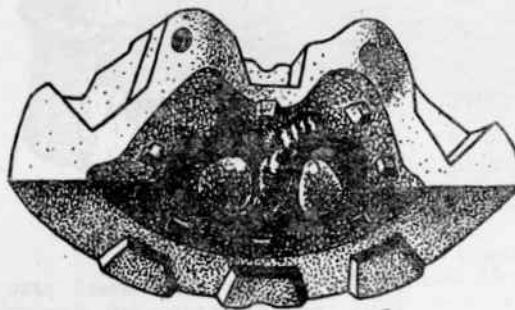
Клеевая форма и отливка черепа. Раскрытая форма. Лицевая часть.
